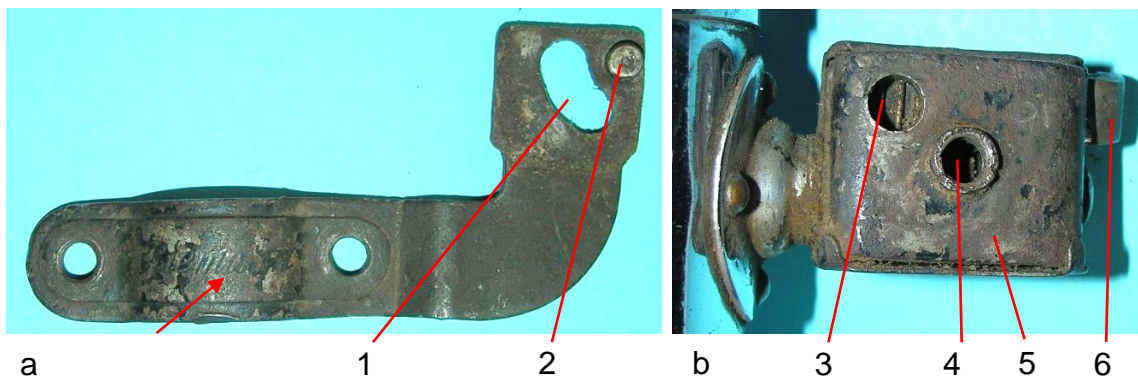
Montagehilfen: a) Halteransicht mit Firmennamen: 1- Langloch, 2- Zapfen, b) Basisblech: 3- Bohrung für den Zapfen, 4- Gewindebohrung für den Befestigungsbolzen, 5- Basisblech, 6- Kulissenriegel
